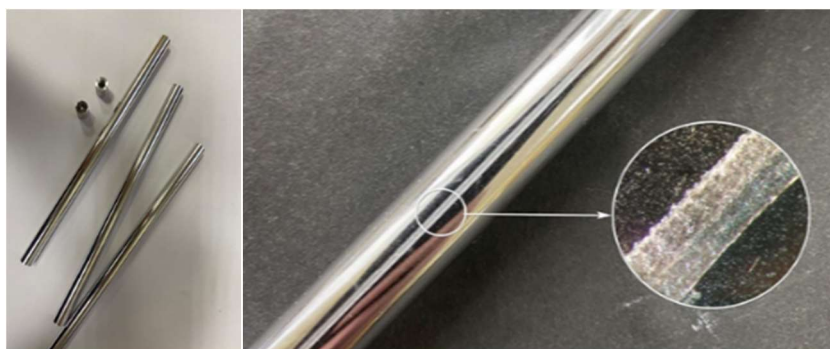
Сварной шов трубки из лавсана с покрытием  $B_4C$  на внутренней стороне цилиндра.
